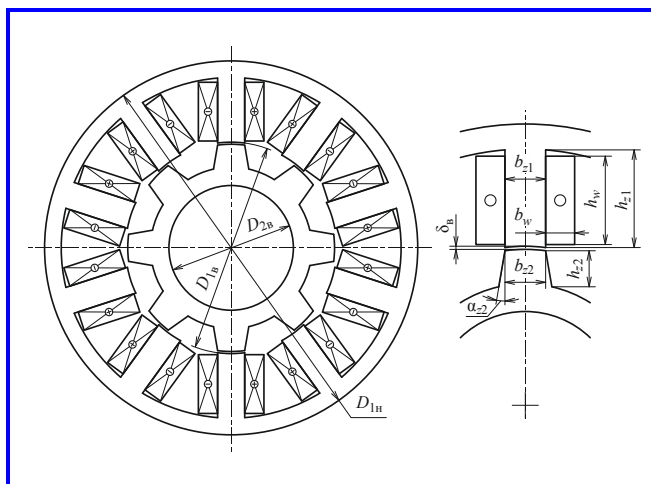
Эскиз активной части вентильно-индукторной электрической машины для устройства натяжения намоточного станка
